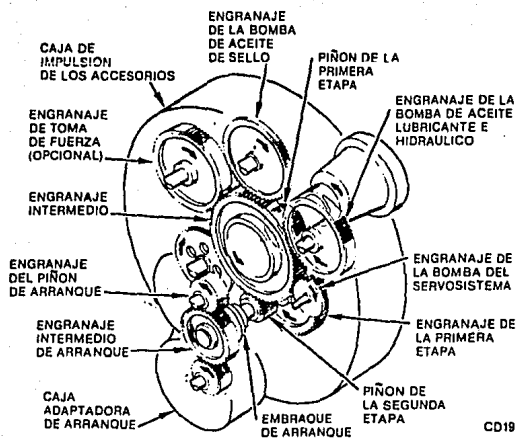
Sistema de engranajes del conjunto de impulsión de los accesorios
